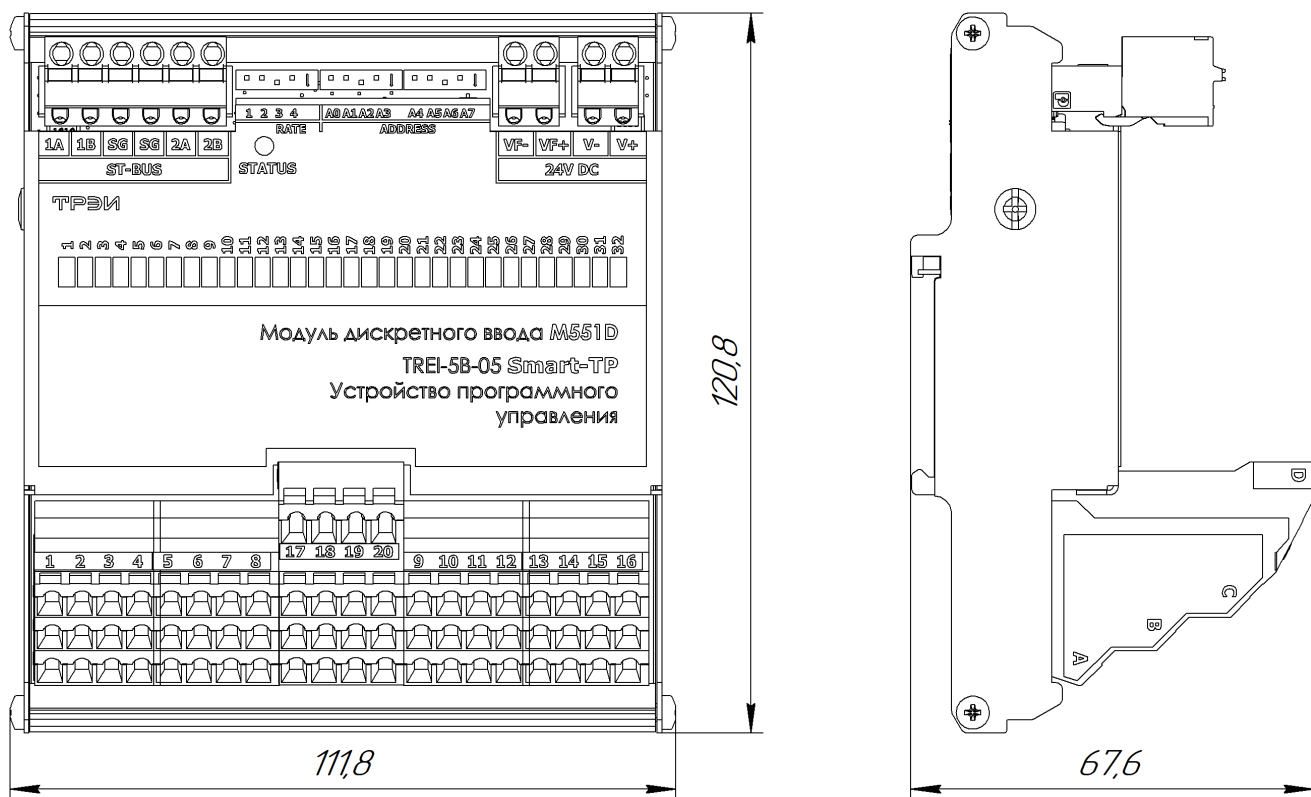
Чертеж общего вида M551D с указанием габаритных и присоединительных размеров
